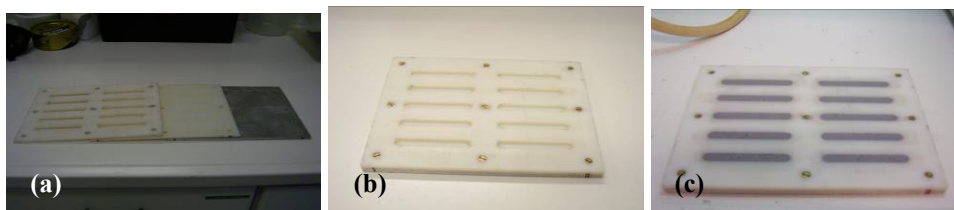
Molde (a) partes do molde; (b) molde montado; (c) molde preenchido com resina
